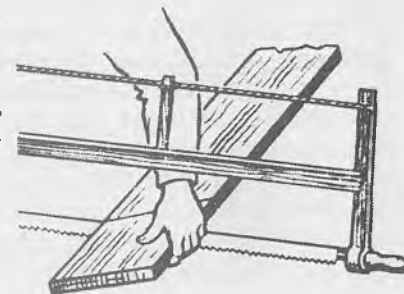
Поддержание рукой отпиливаемой части заготовки для предупреждения брака при пилении
